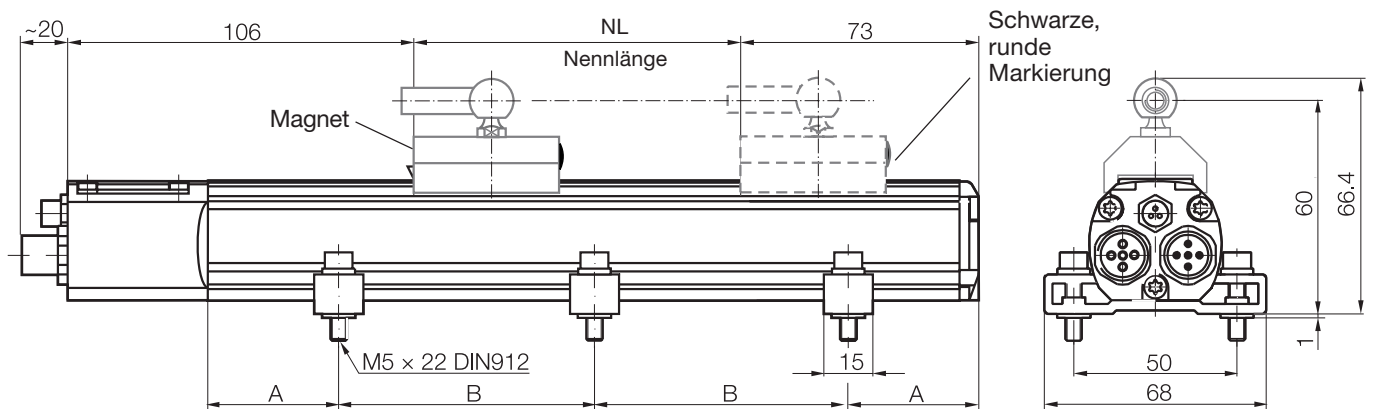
Maßzeichnung (Wegaufnehmer BTL5...P-S103 mit geführtem Positionsgeber BTL5-F-2814-1S)
